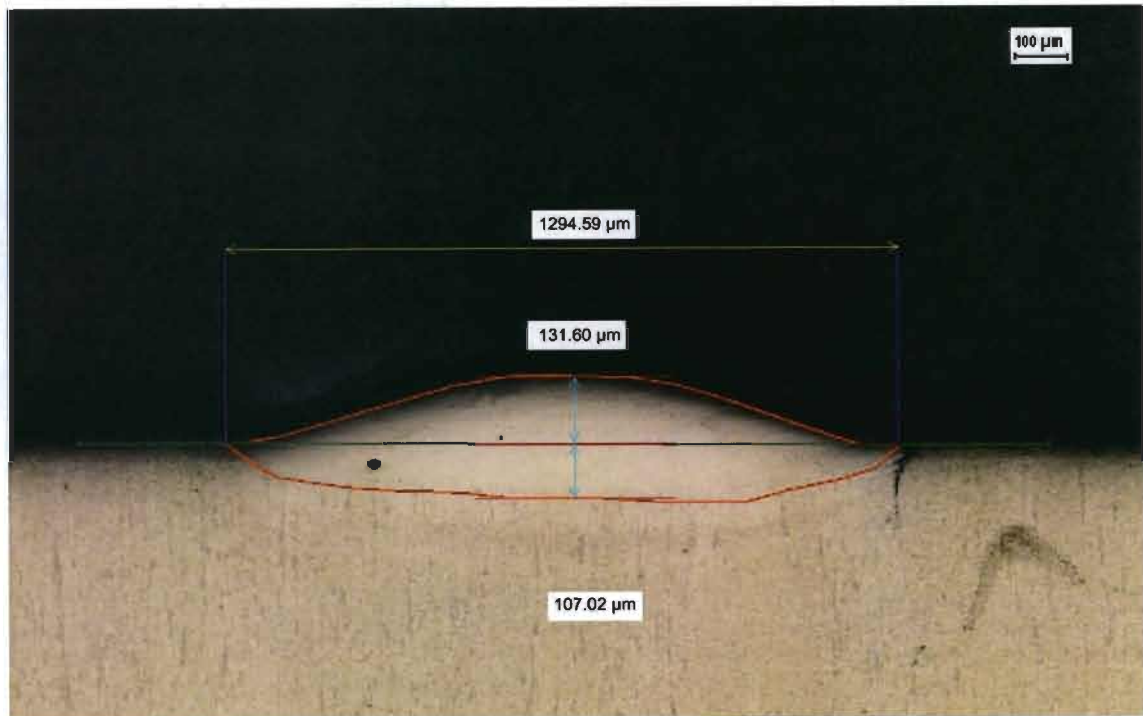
9 Cordón de soldadura 5 visto a 5X
